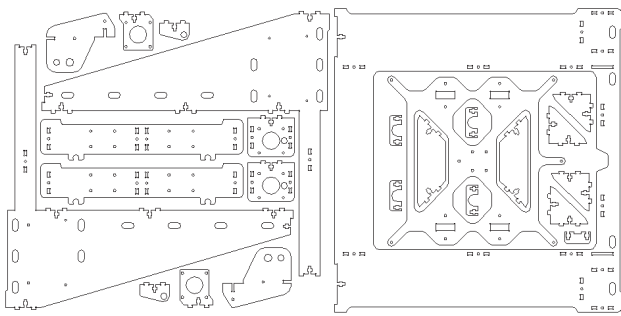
Двовимірний кресленник каркасу 3D принтера
